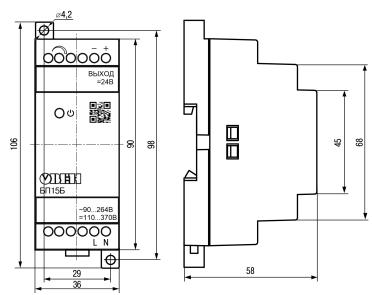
Внешний вид, габаритные и установочные размеры прибора
